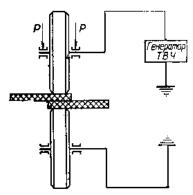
Схема роликовой сварки пластмасс токами высокой частоты.
